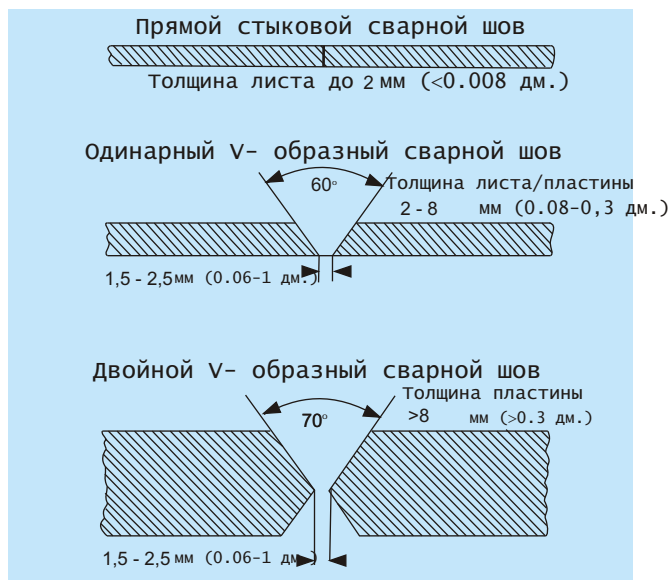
Подготовка шва для аргоно-дуговой сварки
